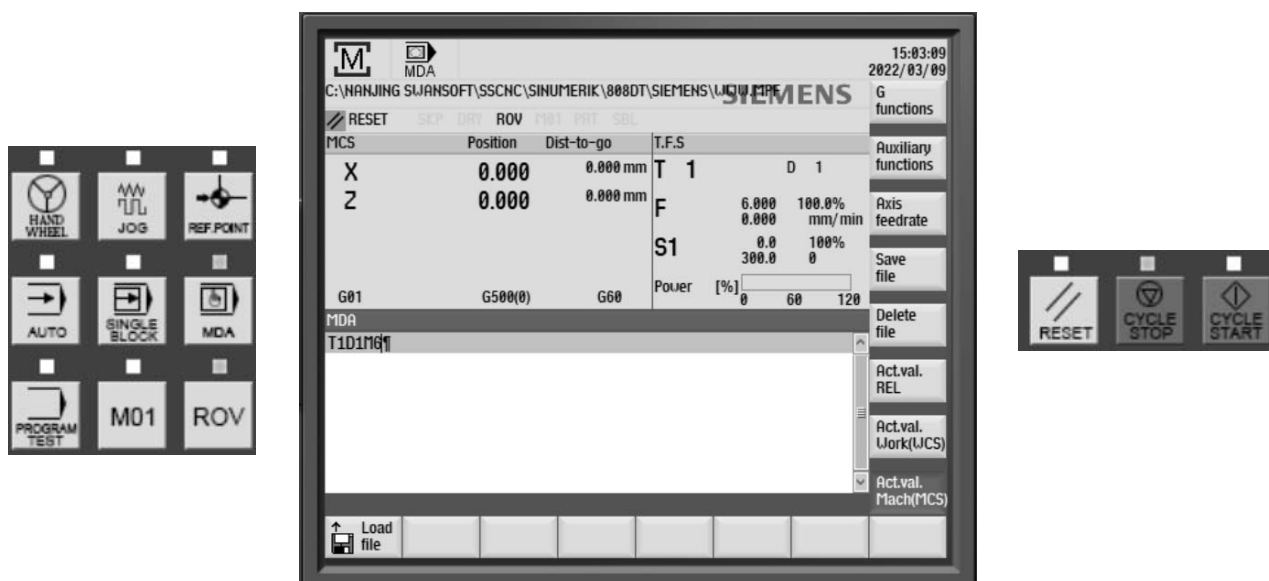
Установка инструмента из позиции T1 в рабочее положение
